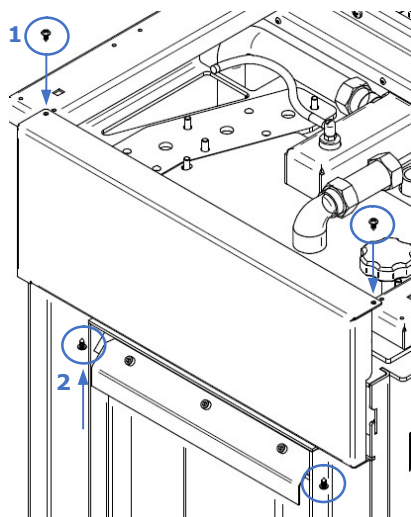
Montaje de la tapa frontal Hidro 17 kW y 23 kW
